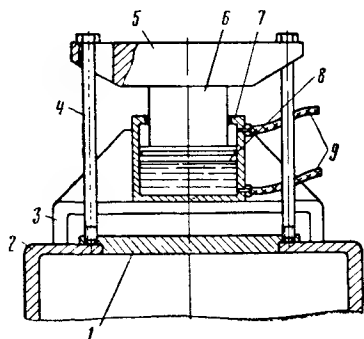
Схема гидравлического приспособления для выпрессовки подшипниковых щитов из остовов двигателей:
